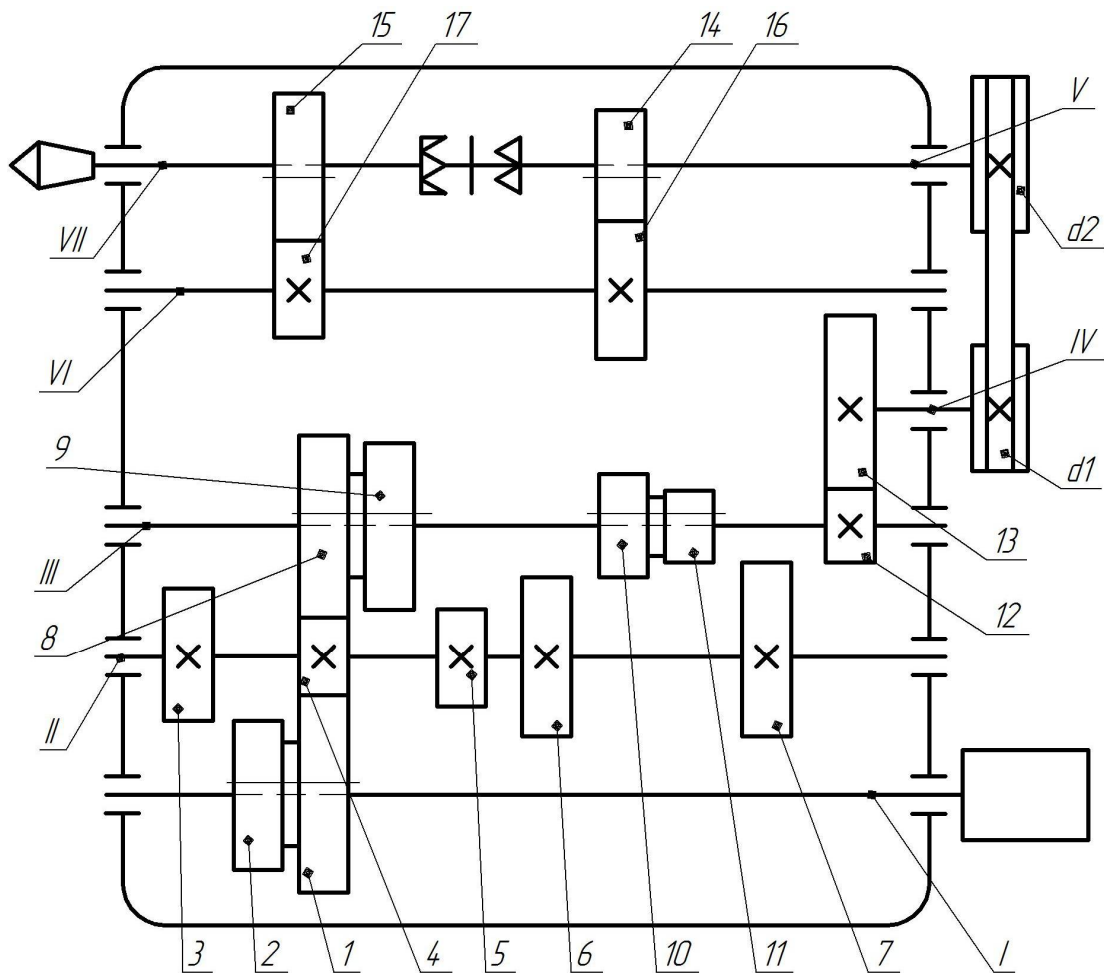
Кінематична схема коробки швидкостей верстата БН81Г
